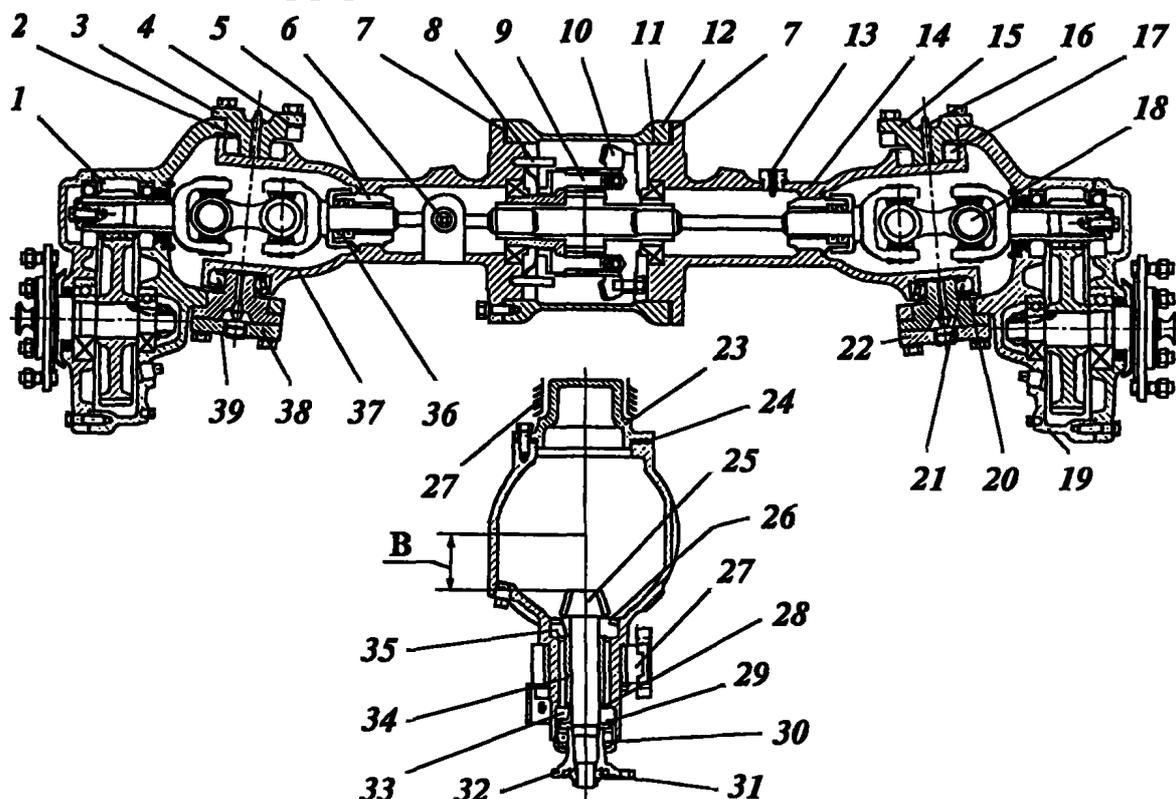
Передний ведущий мост: 1 - редуктор левый; 2 - крышка; 3 - рычаг поворотный; 4, 7, 26, 28 - прокладки регулировочные; 5 - обойма; 6 - пробка; 8 - штифт; 9-дифференциал; 10 - шестерня ведомая; 11, 20 - кольца; 12-корпус; 13-сапун; 14, 37 - рукава; 15 - палец подвески; 16 - масленка; 17, 21, 33, 35 - подшипники; 18 - шарнир карданный; 19 - редуктор правый; 22, 38 - рычаги; 23, 32 - фланцы; 24 - прокладка; 25 - шестерня ведущая; 27 - кронштейн; 29 - кольцо маслоотгонное; 30, 36 - манжеты; 31 -гайка; 34 - втулка; 39 - заглушка
